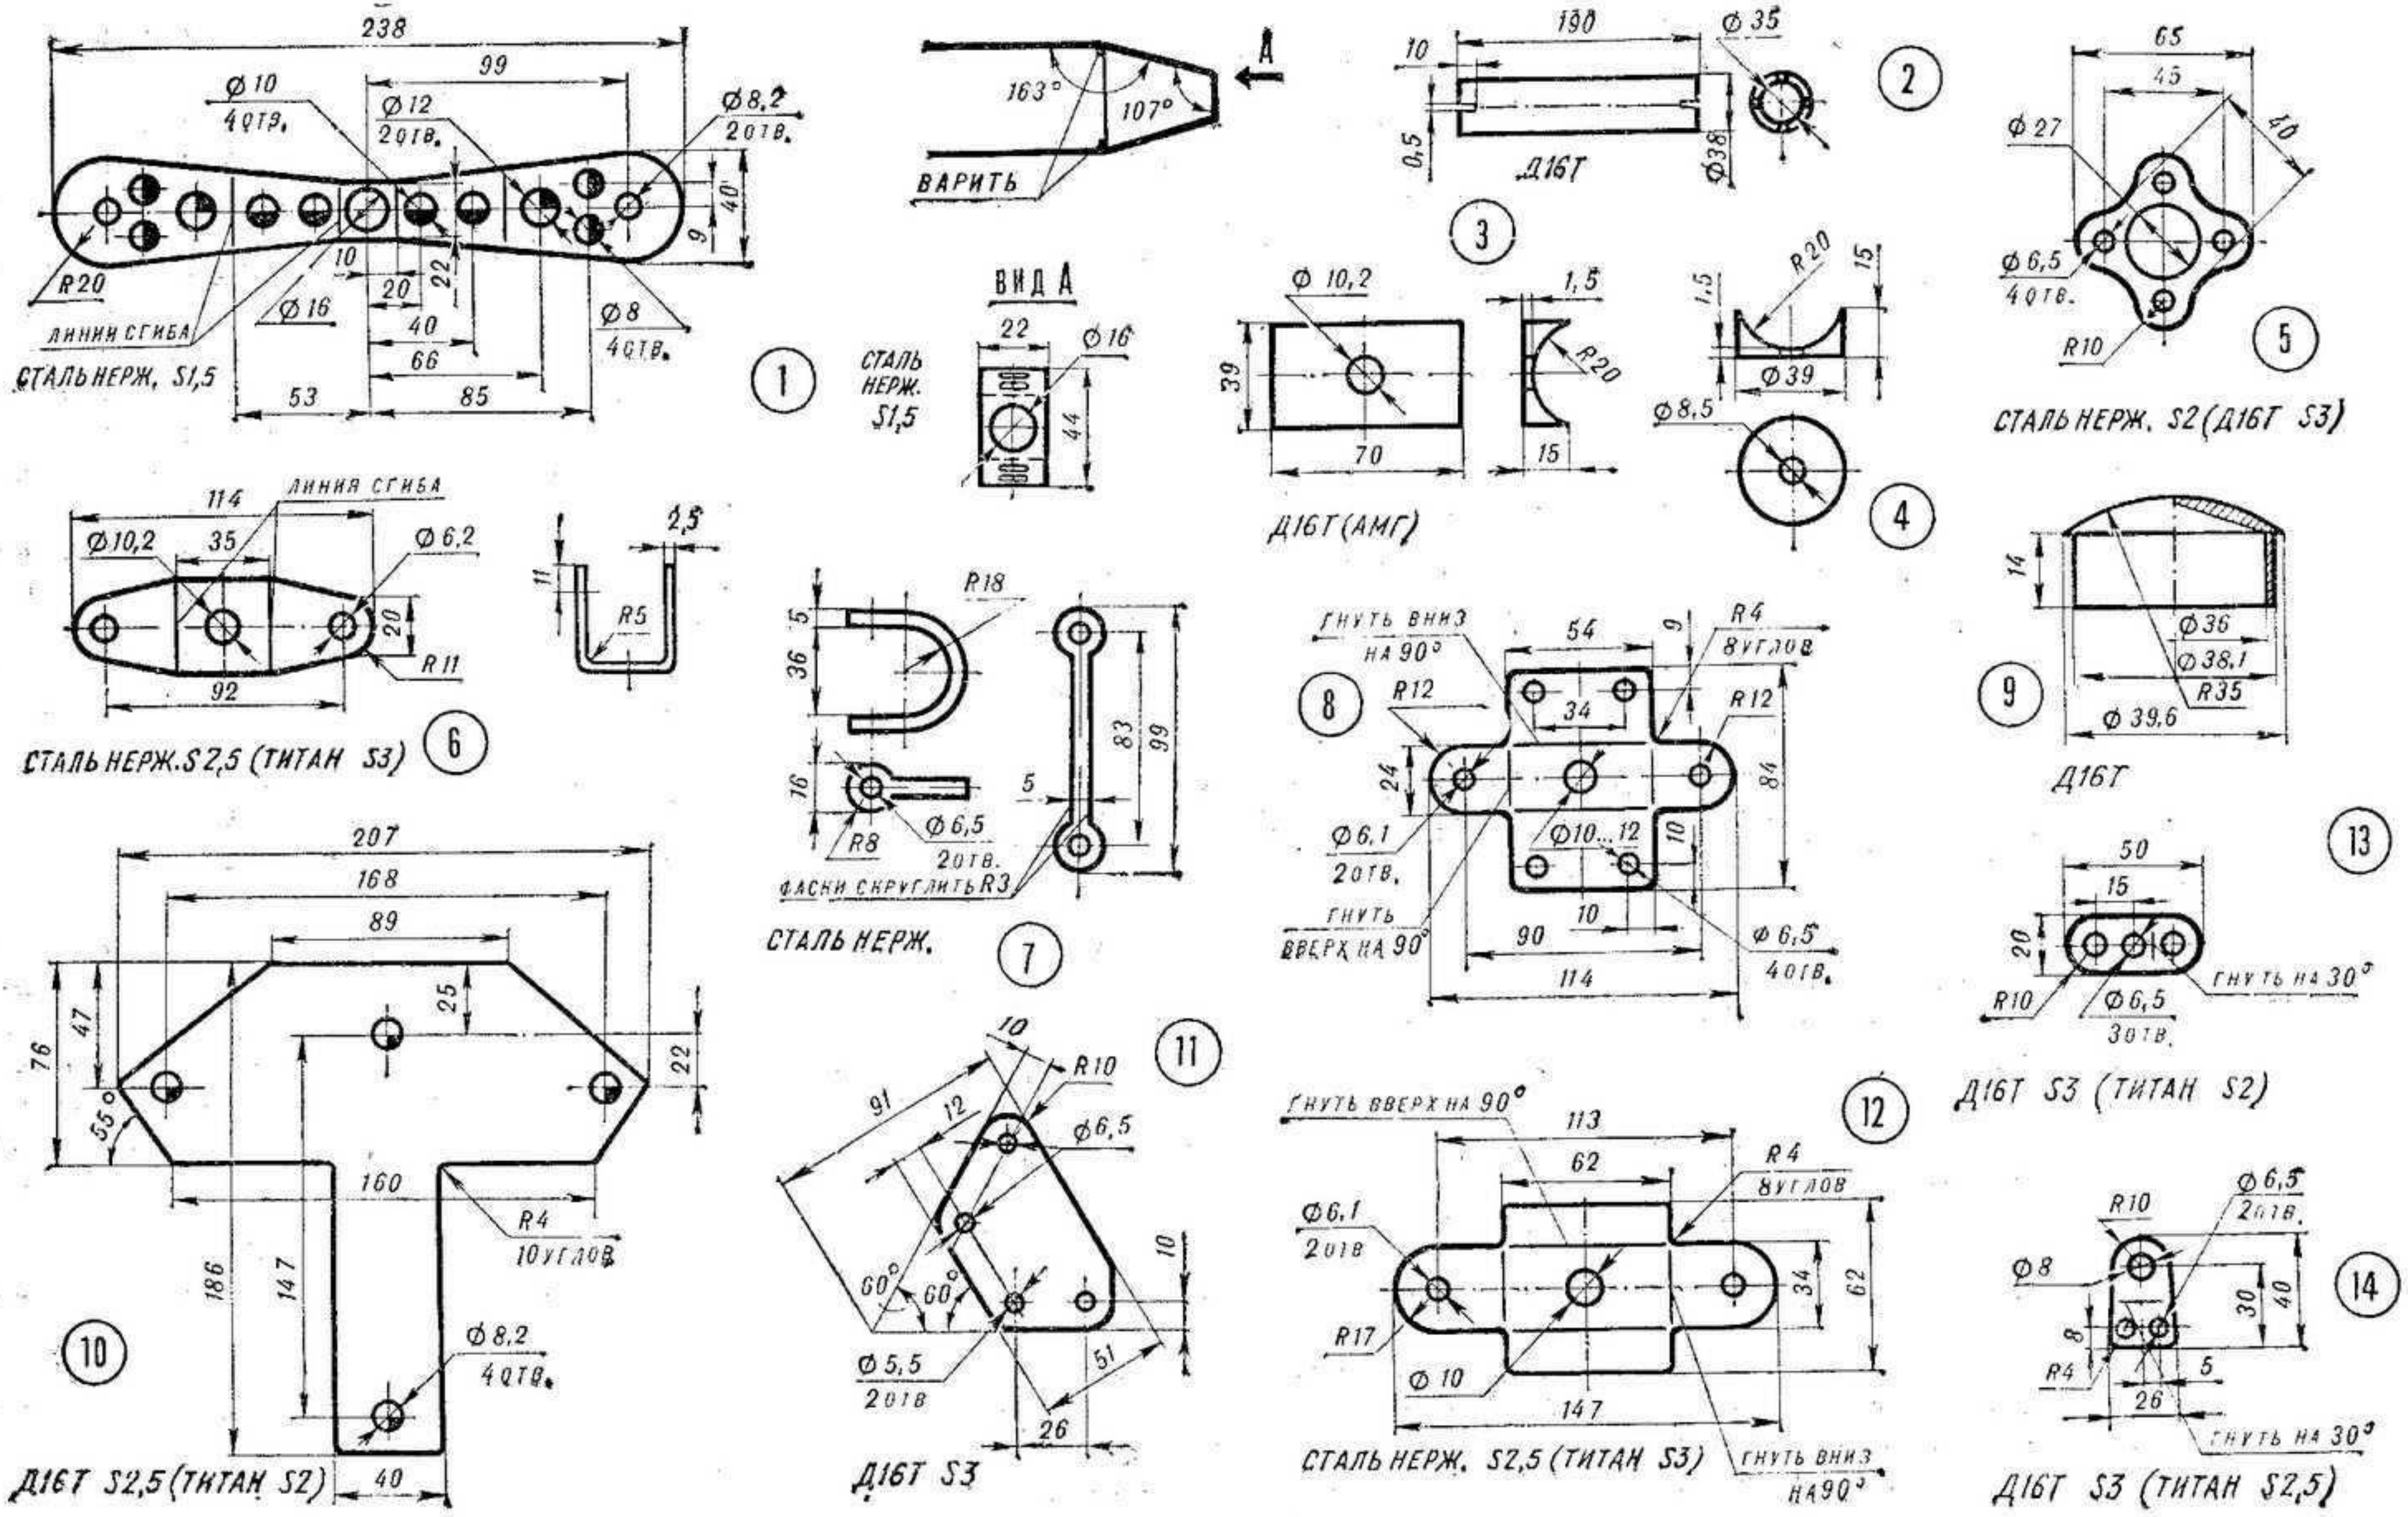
Металлические детали каркаса: 1 — кронштейн крепления аутриггеров: развертка, сварка, перегородка, 2 — проставка для стыковки труб, 3 — прокладка, 4 — фигурная уплотнительная шайба, 5 — крестовина мачты, 6 — скоба крепления мачты, 7 — дужка, 8 — кронштейн № 1 центрального узла, 9 — заглушка трубы, 10 — пластина носового узла, 11 — щечка рулевой трапеции, 12 — кронштейн № 2 центрального узла, 13 — пряжка крепления тросиков боковых труб, 14 — ушко крепления тросов к носовому узлу.
